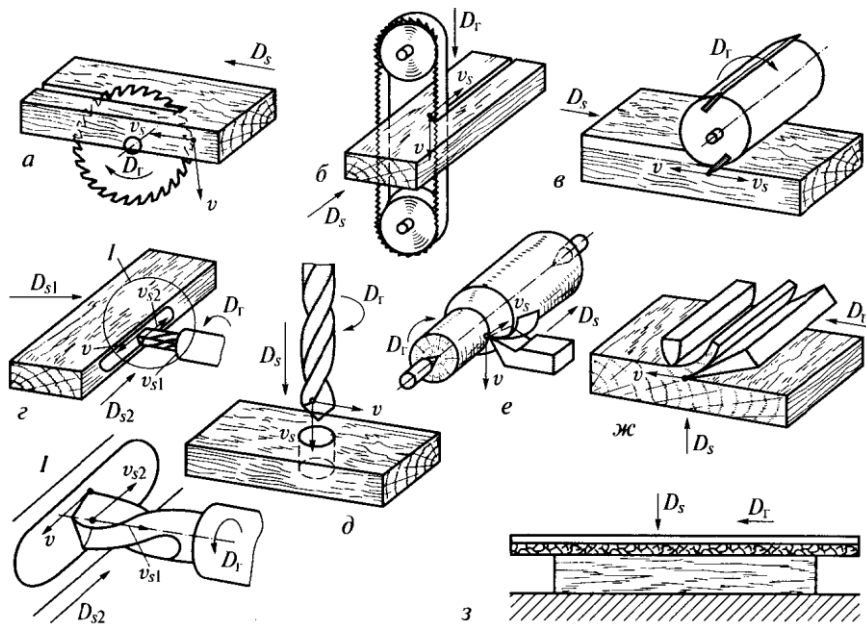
Процеси різання деревини: *a* – пиляння круглою пилкою; *б* – пиляння стрічковою пилкою; *в* – фрезерування; *г* – пазове фрезерування кінцевою фрезою; *д* – свердління; *е* – точіння; *ж* – стругання; *з* – шліфування
